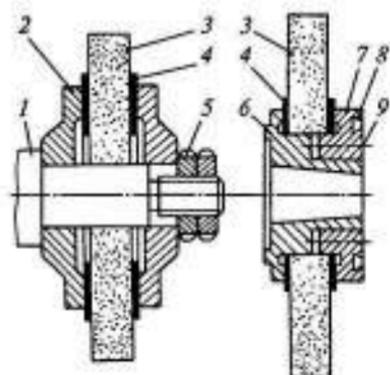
Устройства для установки и крепления шлифовальных кругов:
